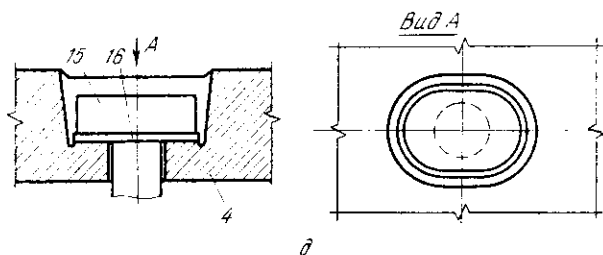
Металлическая футеровка цилиндрической части барабана:
